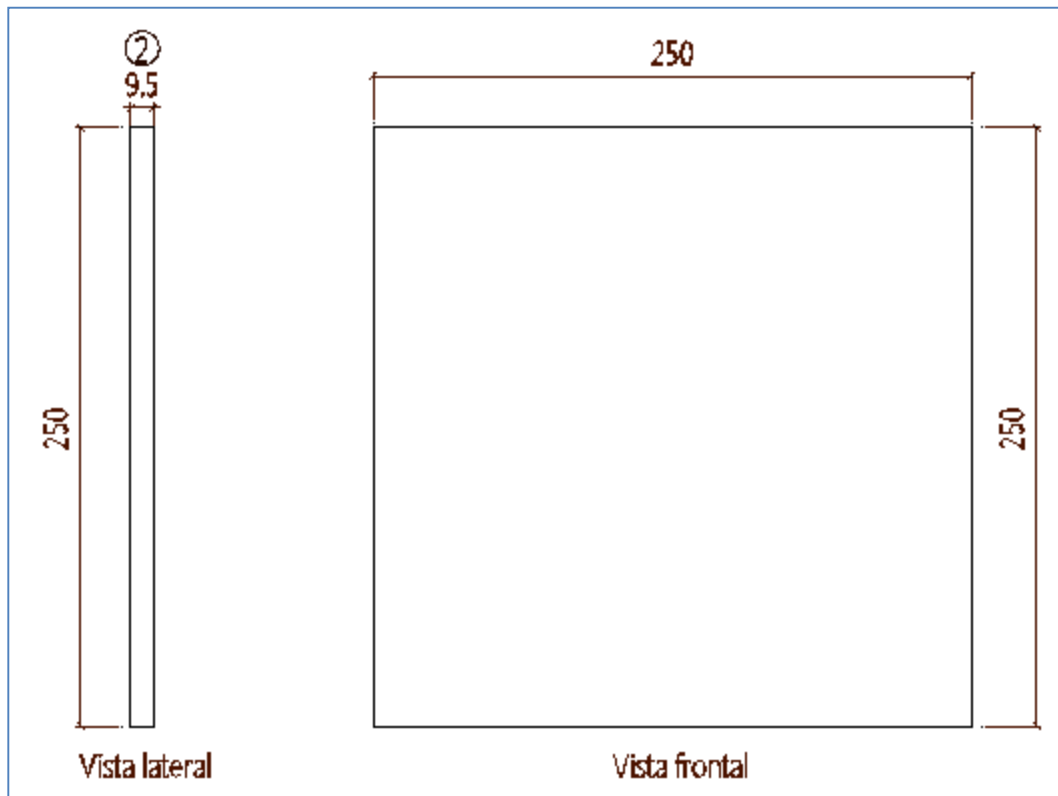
Detalle despiece pieza No.2 modelo 1 tensión.
